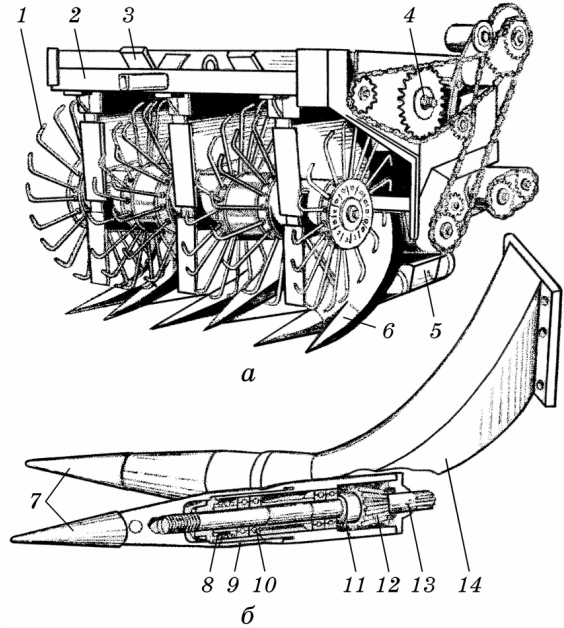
Викопувальний пристрій коренезбиральної машини МКК-6-02:
